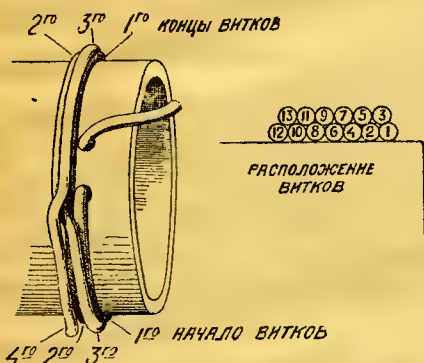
Способ намотки и расположение витков двуслойной катушки.
